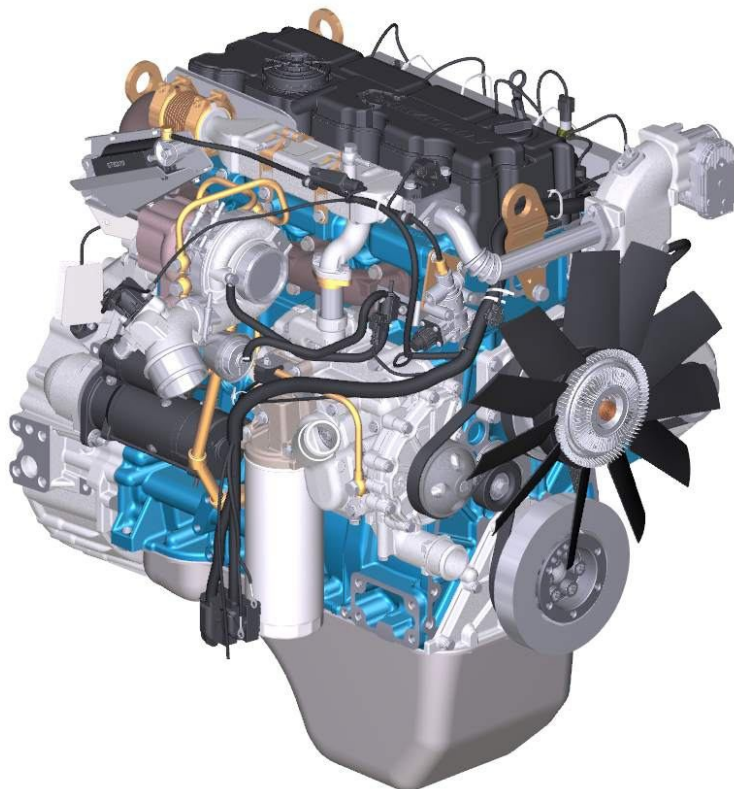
Общий вид двигателя ЯМЗ-53444-20 (Лист 2 из 2)
